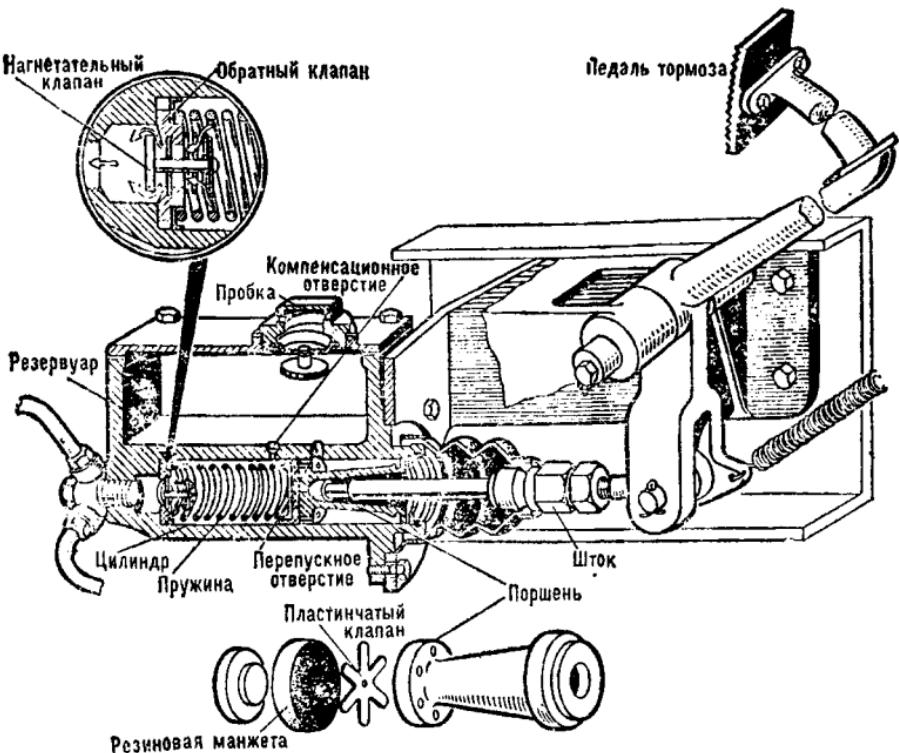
Главный тормозной цилиндр автомобиля ГАЗ-53-12
